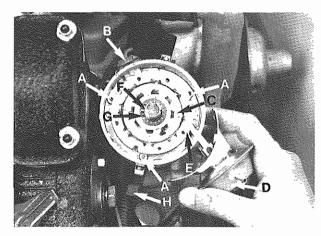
A - Viti di fissaggio statore - Stator fixing screws
